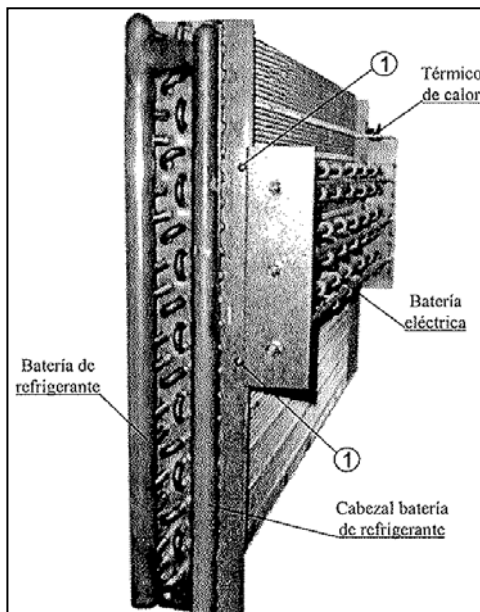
Sujeción de Batería Eléctrica a la Batería Refrigerante.
